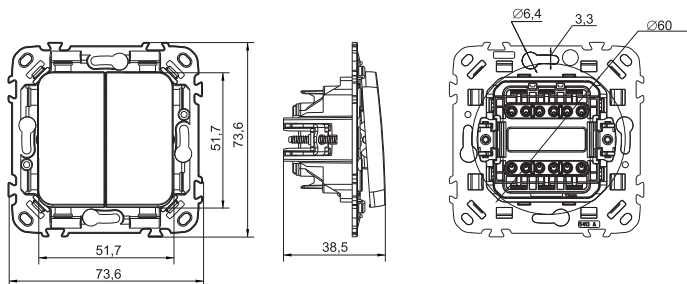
Габаритные и установочные размеры двухклавишных выключателей /
